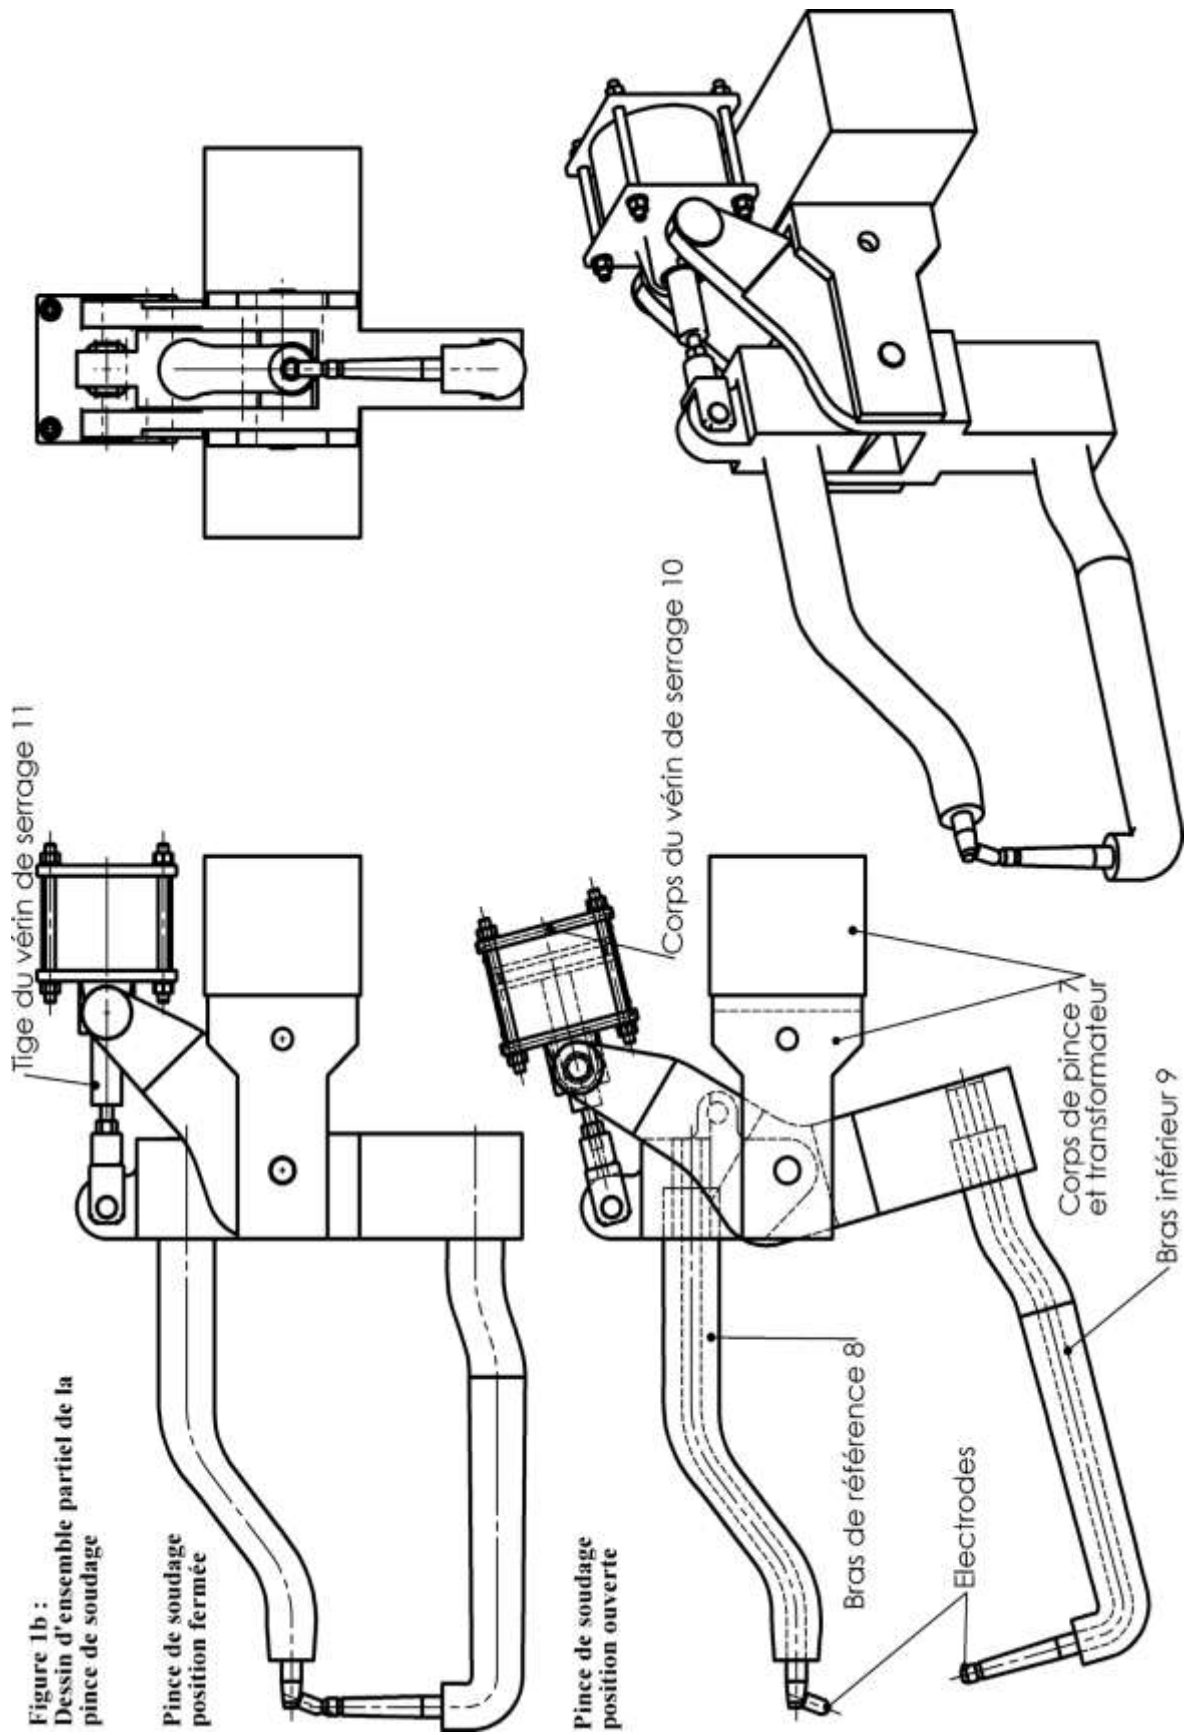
dessin d'ensemble partiel de la pince de soudage [31].
